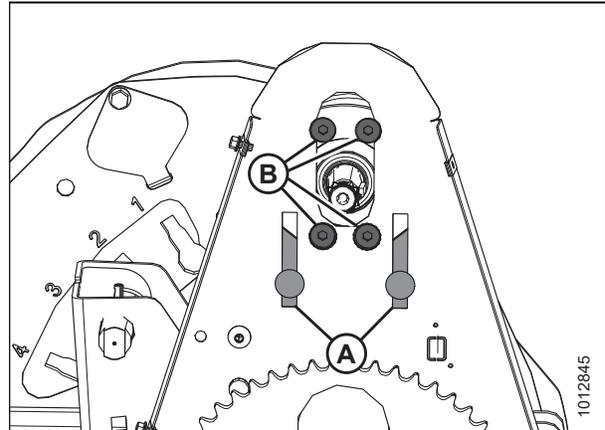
Befestigungsbohrungen des Haspelantriebmotors
